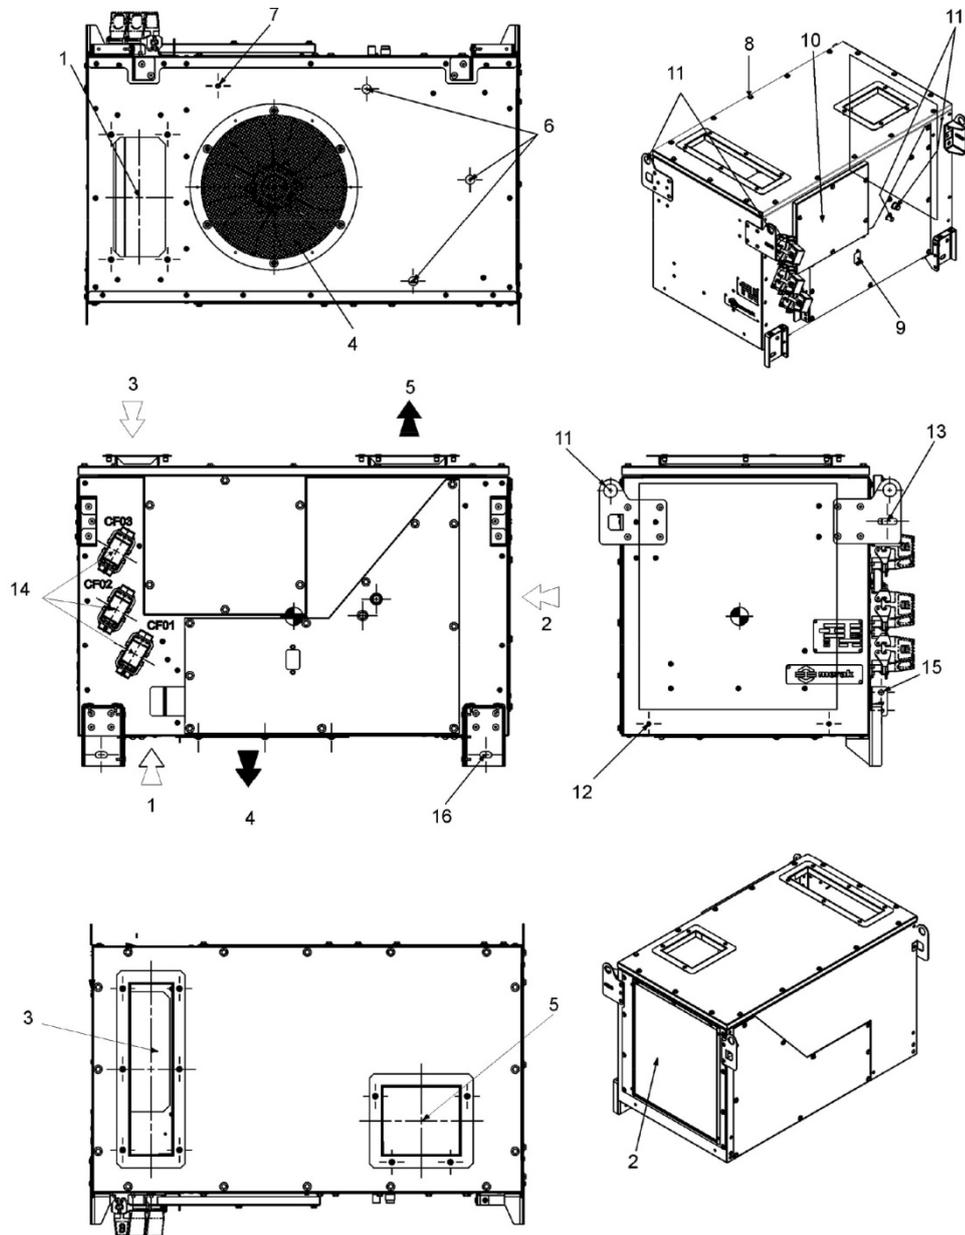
Vista del modulo HVAC di cabina con dettaglio estrazione
